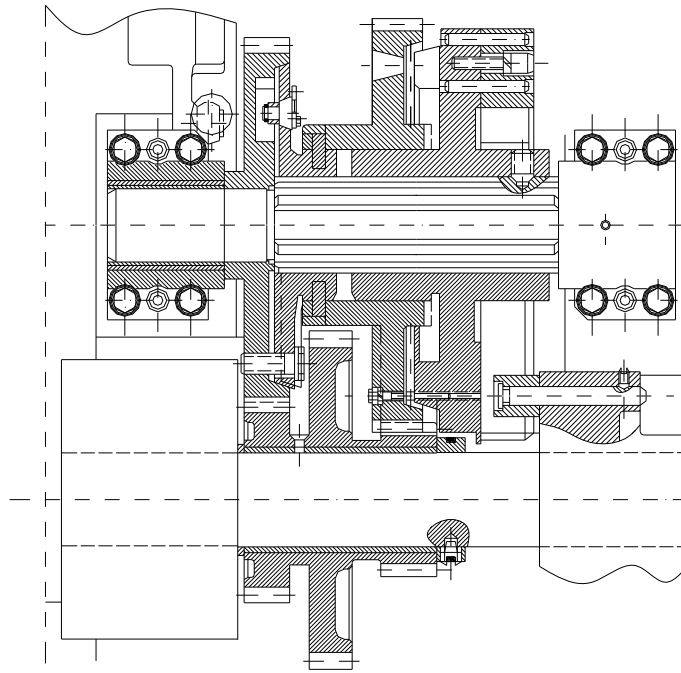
Схема мальтійського механізму приводу ШБ (вид збоку)
